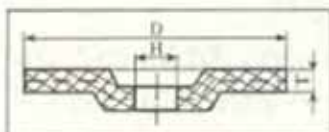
Профиль для шлифовки, обдирки, зачистки сварных швов, прорезки пазов.
